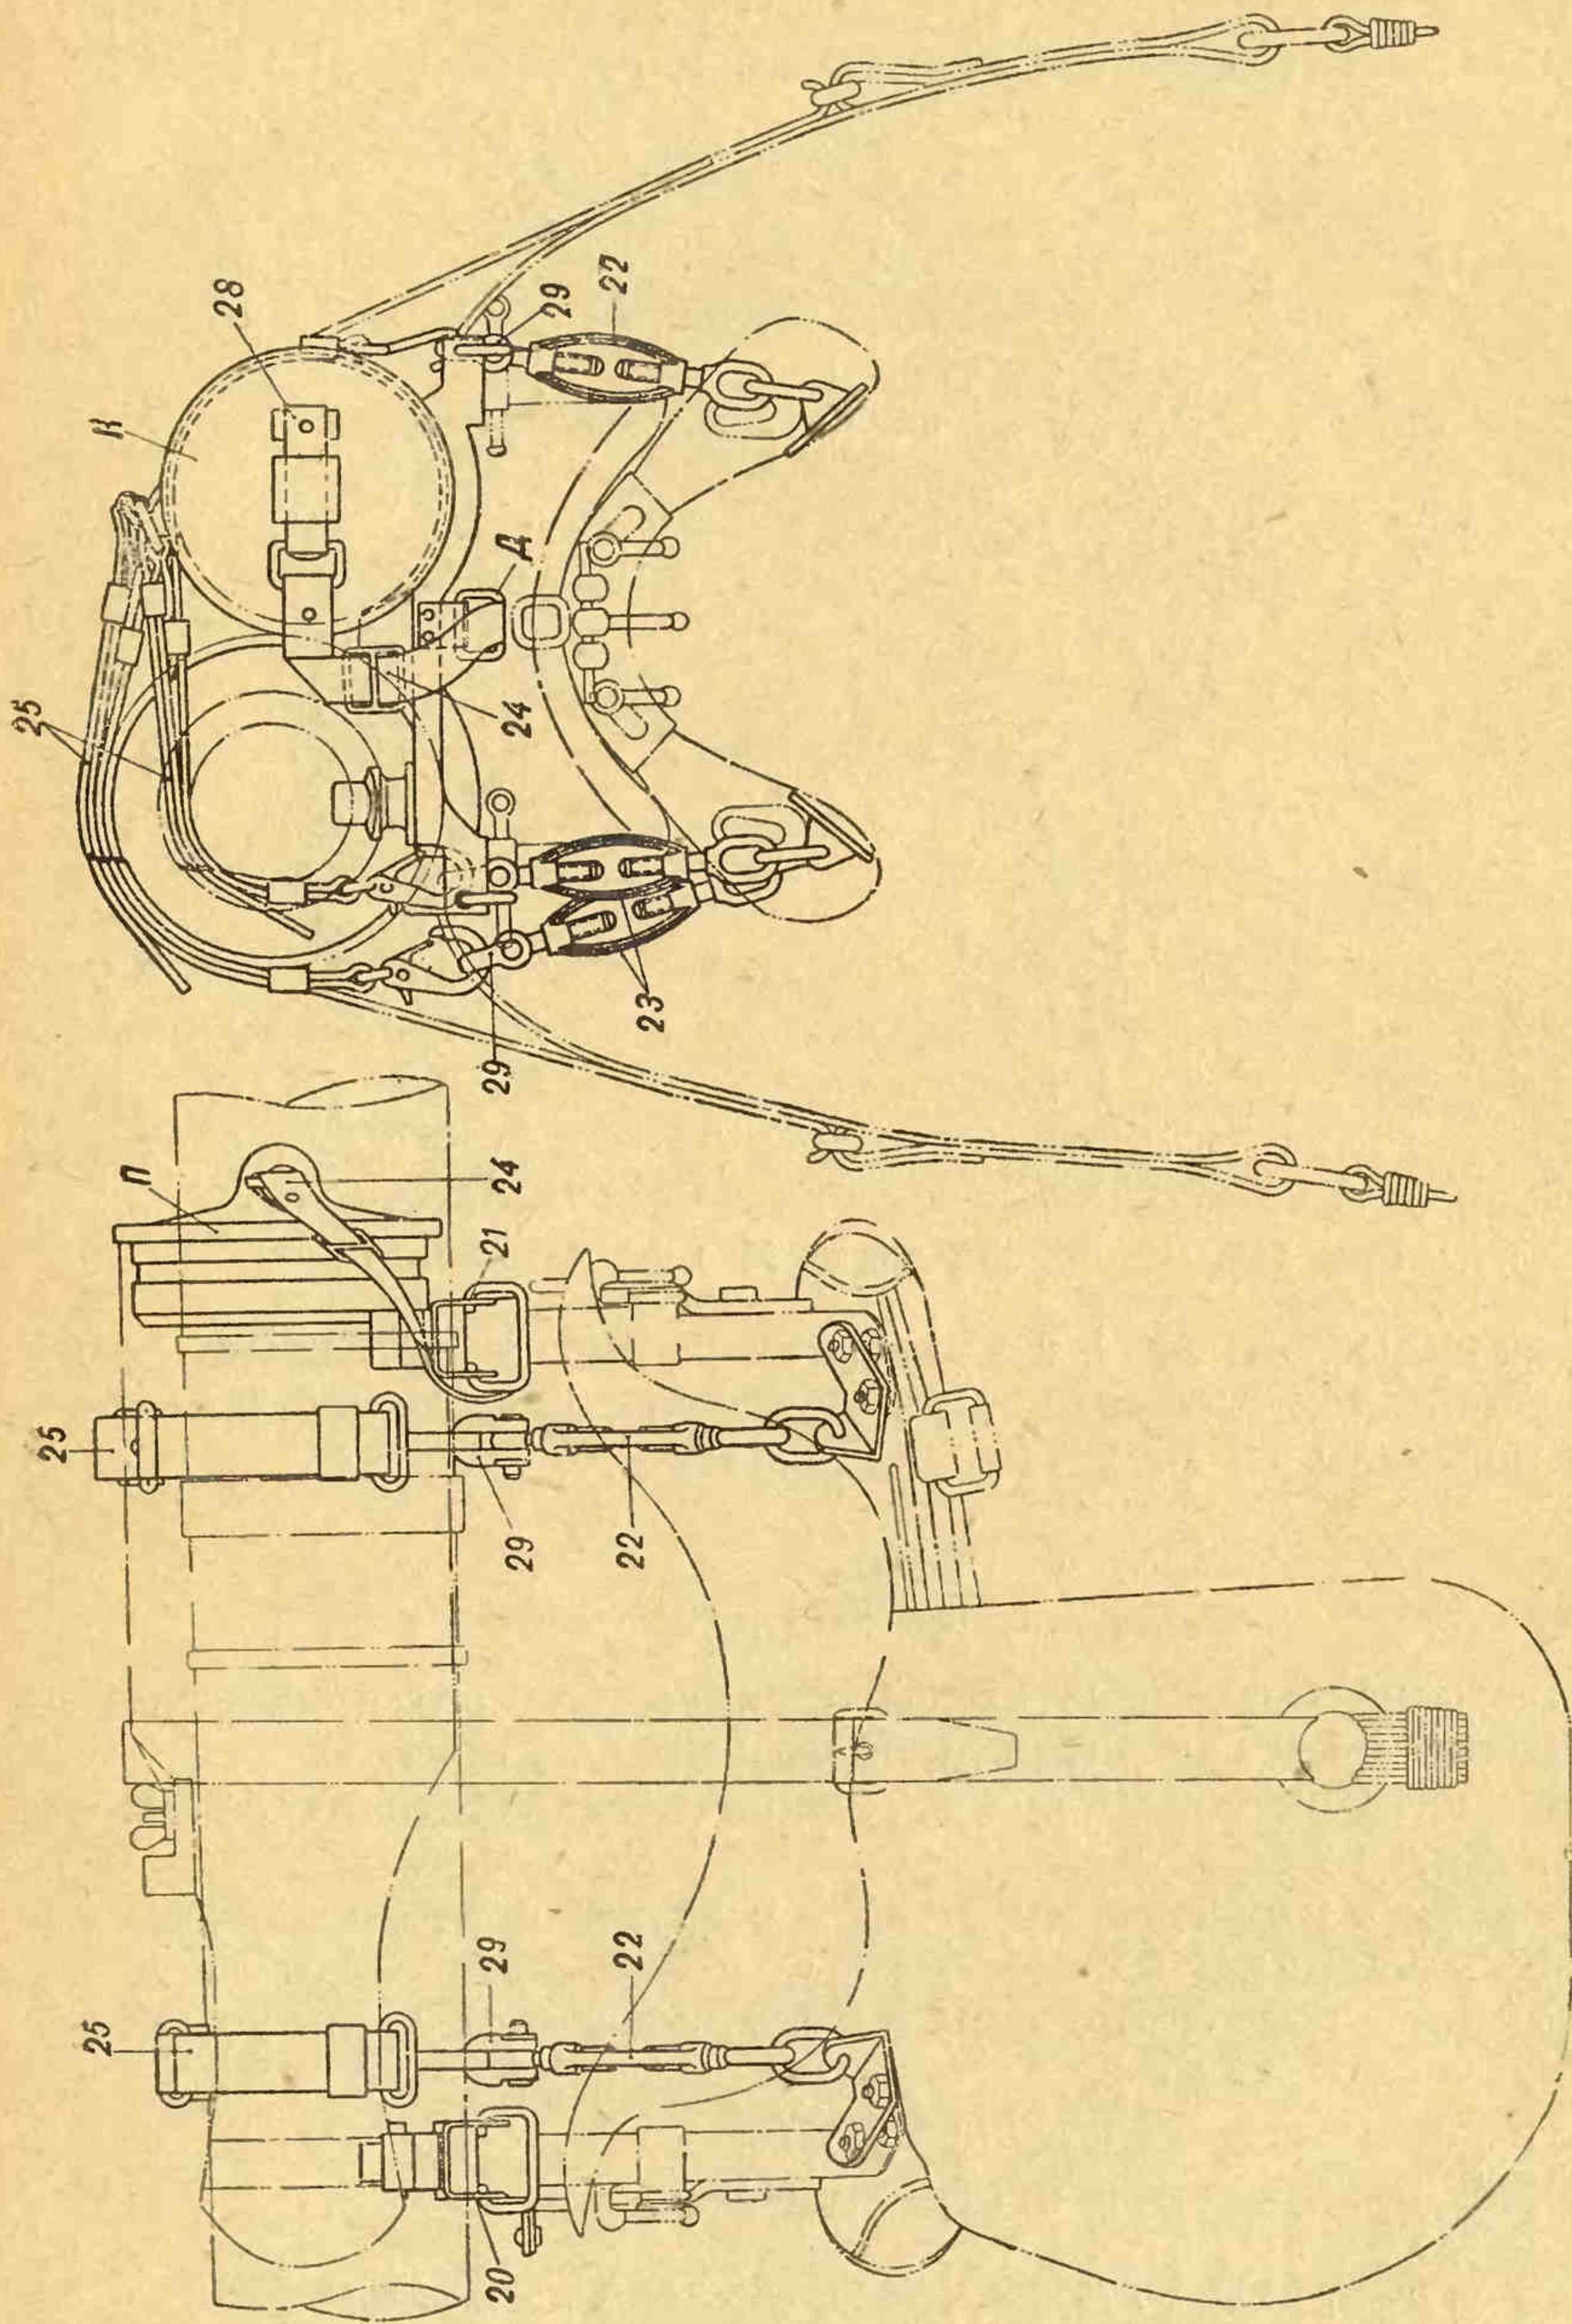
Укладочное приспособление № 2 для ствола п казенника:
